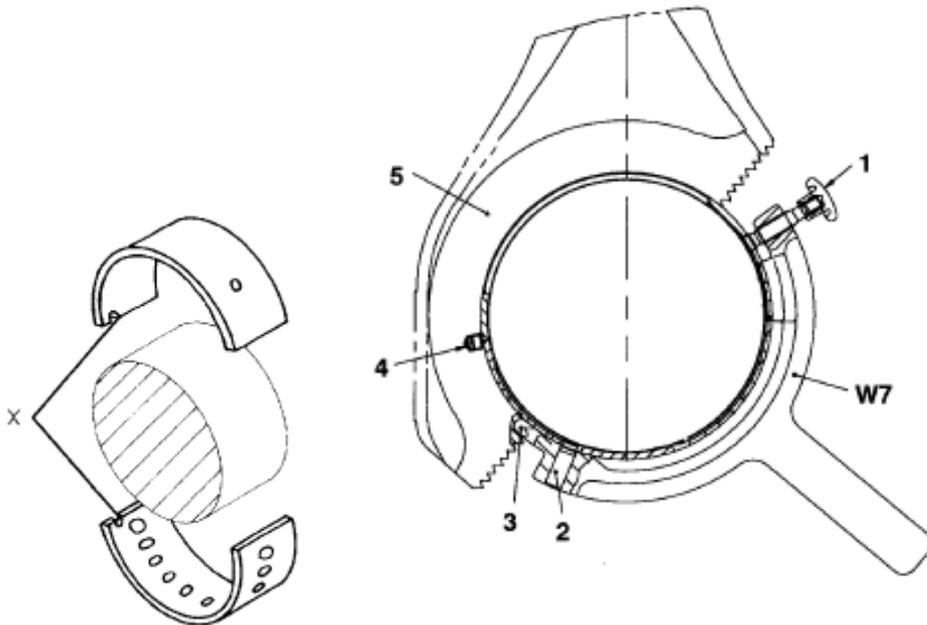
Utilización útil W7, para el montaje de los cojinetes cabeza de biela. (fuente MAK)
